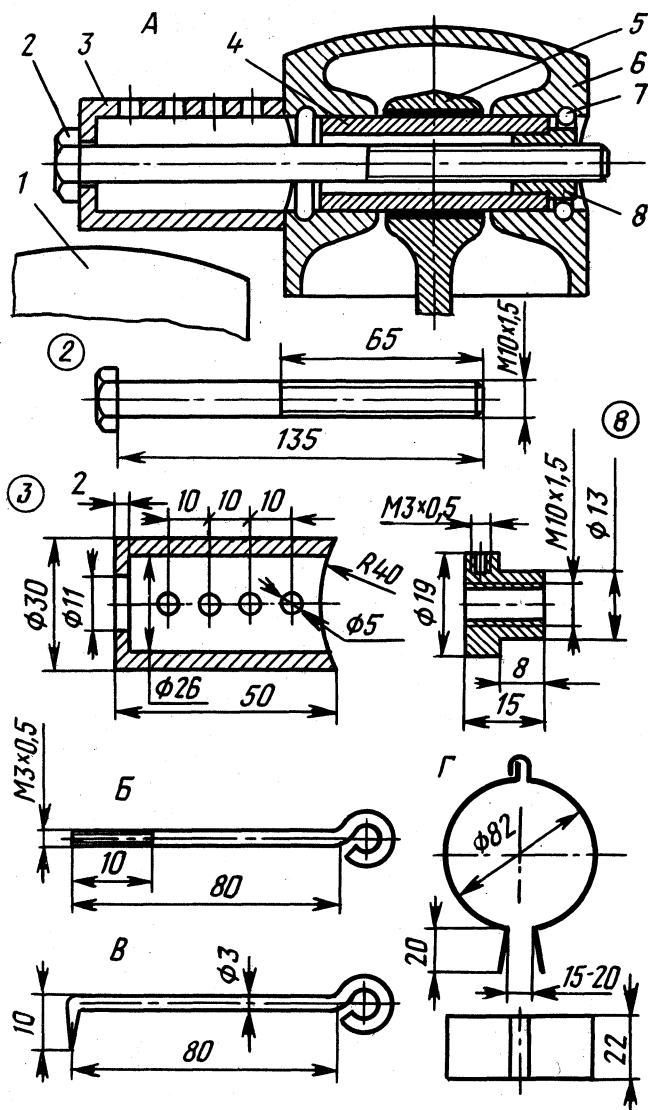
Приспособления, требуемые для замены поршней двигателя «Москвич-412»:
